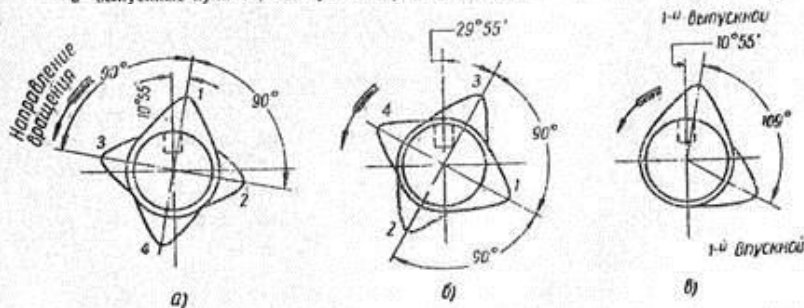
Схема углового расположения кулачков распределительного вала двигателей М-20 и ГАЗ-69 (со стороны переднего конца вала): а — выпускные кулачки, б — впускные кулачки, в — кулачки первого цилиндра.
